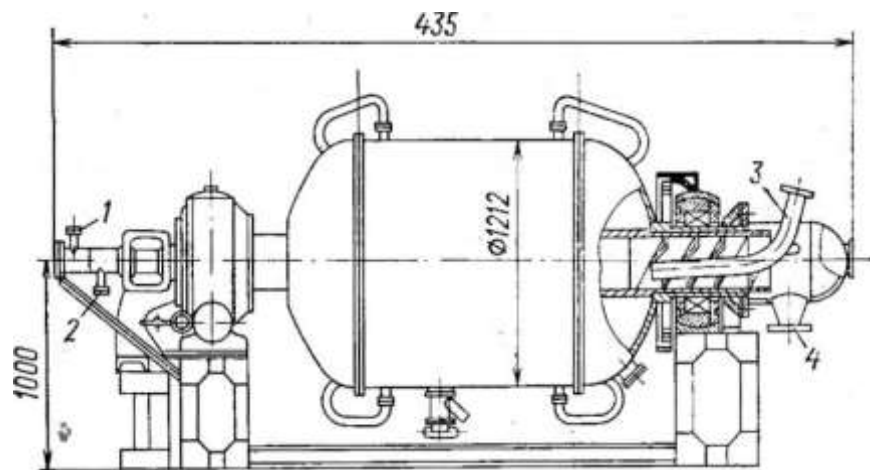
Барабанна вакуумна сушарка типу ВБС з обертовим корпусом:
